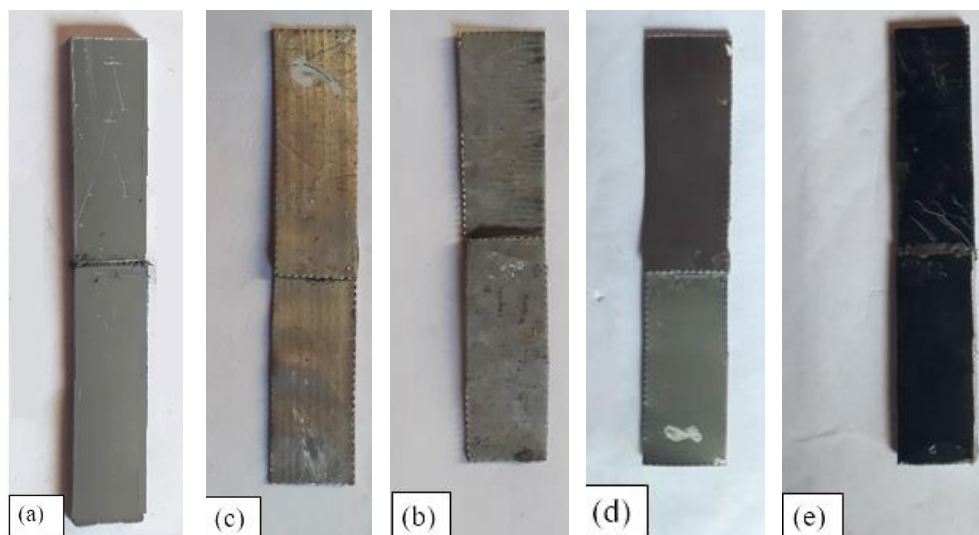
Eprouvettes assemblées par époxy (a) PVC (b) acier galvanisé (c) aluminium (d) acier inox (e) PE.
